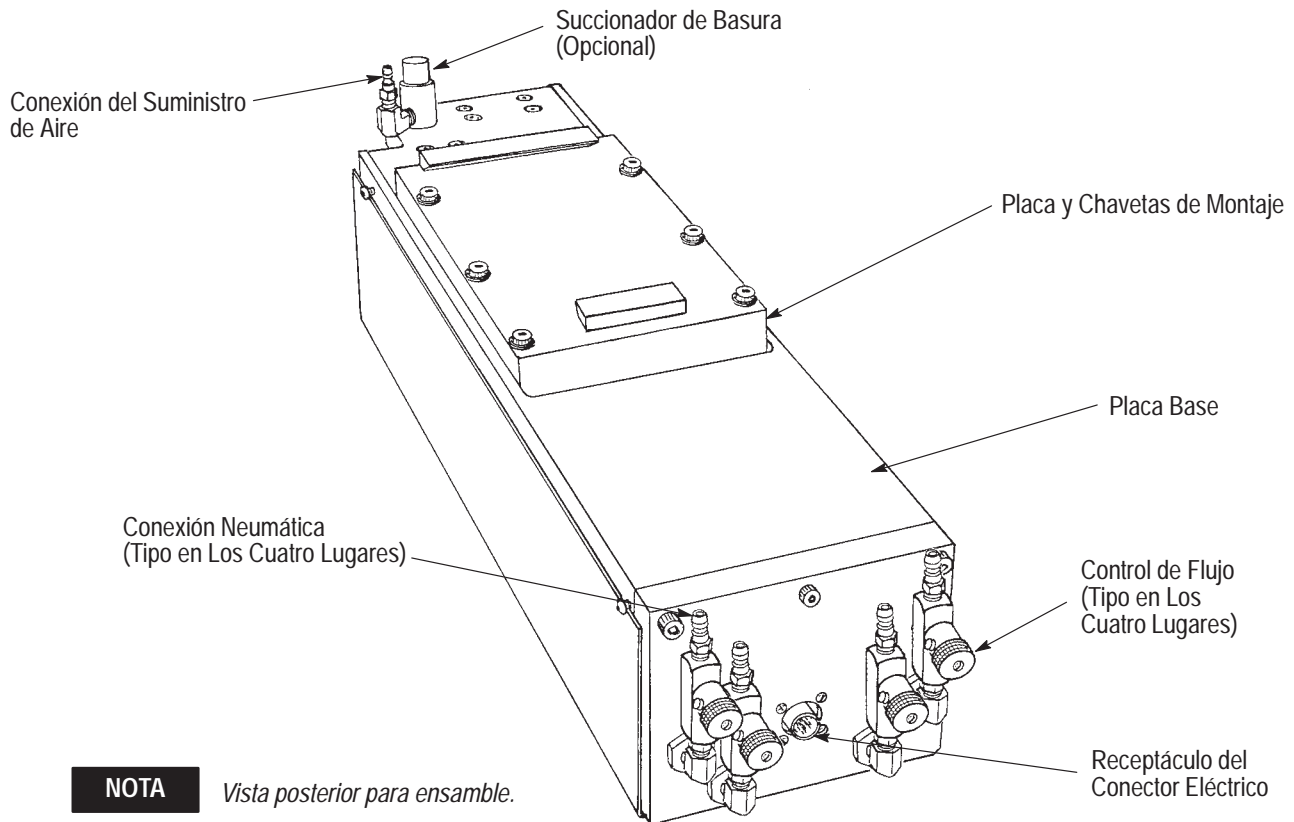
Instalación, Montaje y Conexiones típicas del Ensamblaje
